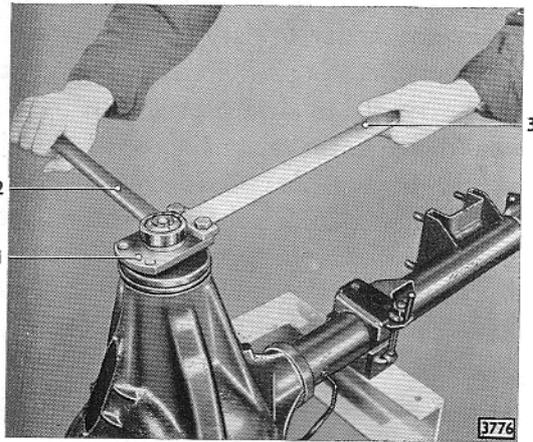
Sechskantmutter für Antriebskegelradflansch lösen
